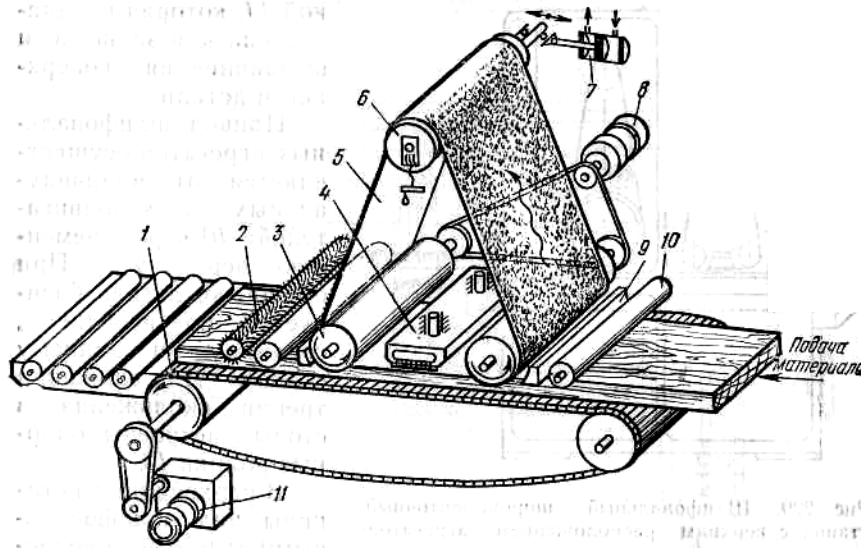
Одноагрегатный широколенточный шлифовальный станок с конвейерной подачей:
